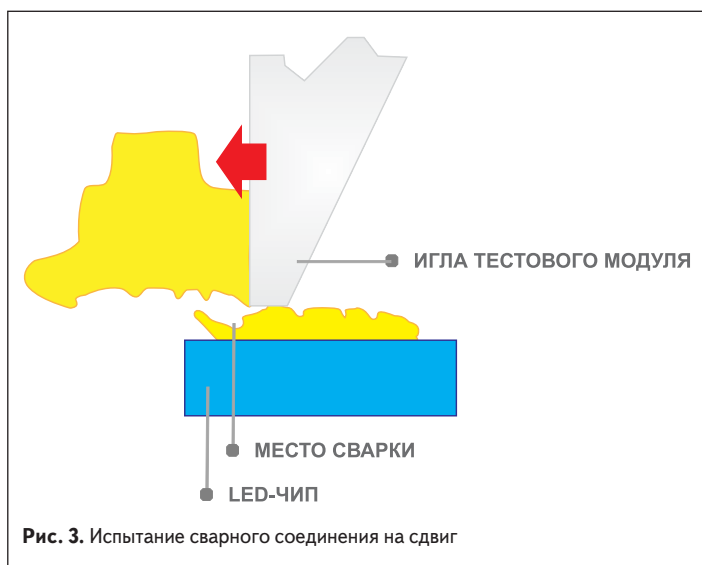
Испытание сварного соединения на сдвиг
